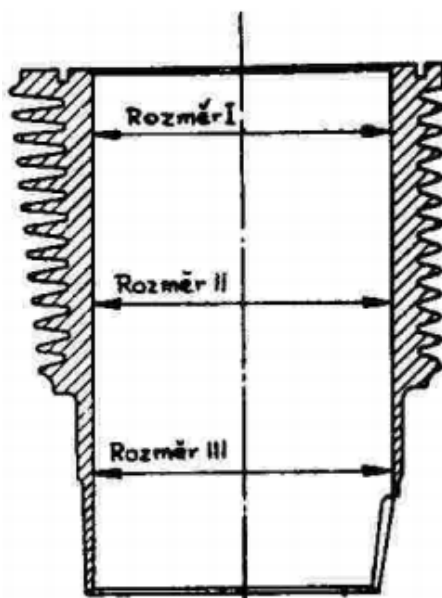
Válec motoru (šipka ukazuje vyražené písmeno, označující toleranční třídu)
